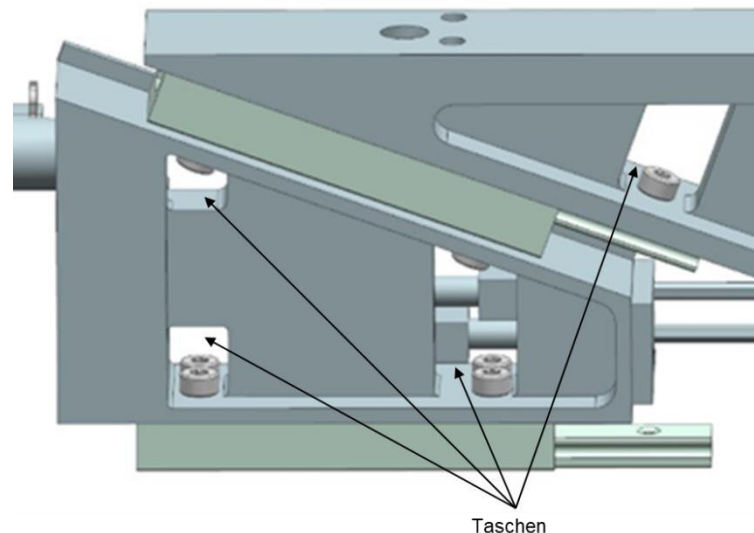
gefräste Taschen für die Montage der Zylinderschrauben
